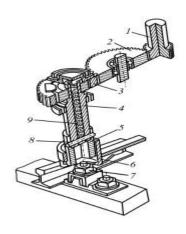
Зубчатая передача и шпиндель ветви трехлучевого редуктора гайковерта: 1, 2 и 3 — солнечное, паразитное и ведомое зубчатые колеса; 4 — шпиндель; 5 — патрон; 6 — искатель; 7 — гайка скрепления; 8 — штифт; 9 — торсионная пружина
